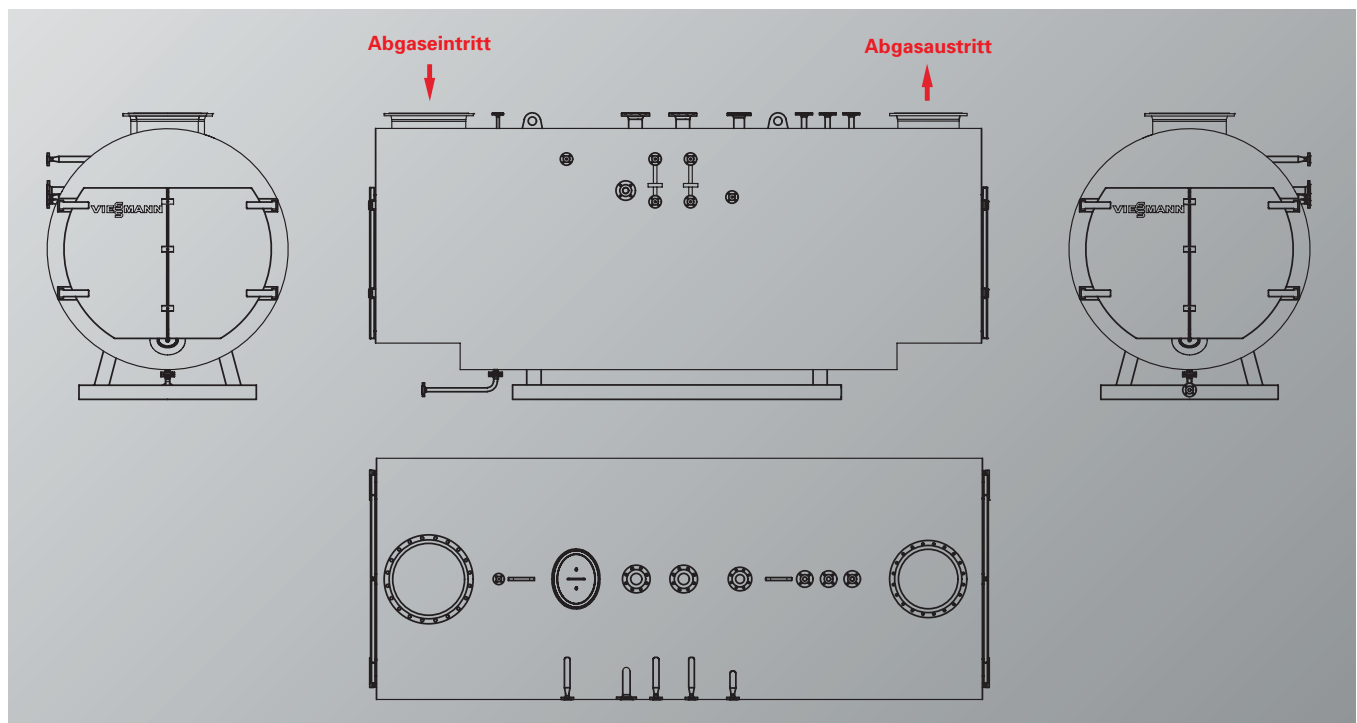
1-Zug-Abhitzeessel zur Dampferzeugung
